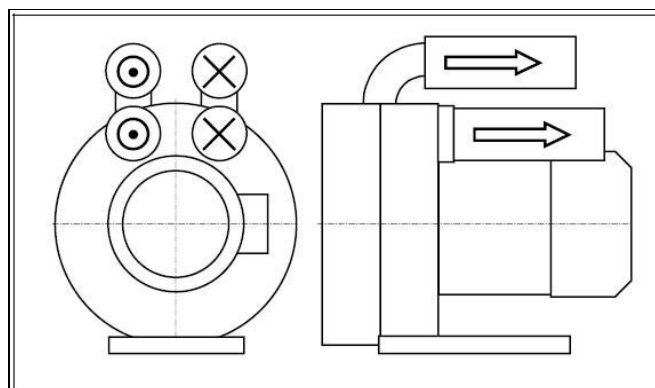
Двухпоточная конструкция вакуумного насоса/компрессора с двумя рабочими колесами.
